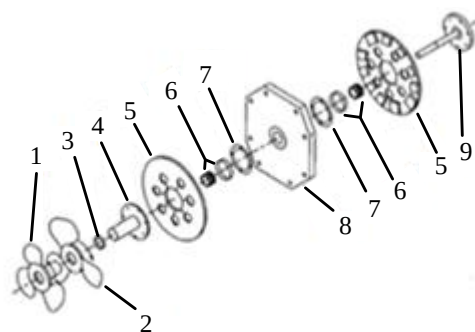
Разобранный вид дисковой машины с противовращающимся ротором: 1 – основной винт; 2 – противовращающийся винт; 3 – радиальный подшипник; 4 – внешний вал; 5 – ротор с ВПМ; 6 – подшипники; 7 – монтажное кольцо; 8 – статор; 9 – внутренний вал
